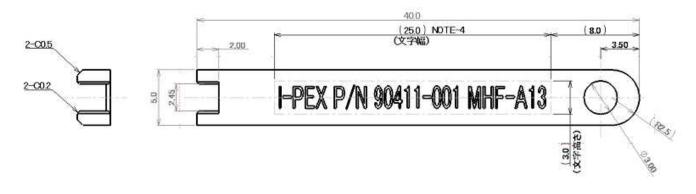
推奨 抜去 JIG (Recommendation: PLUG pull JIG)
